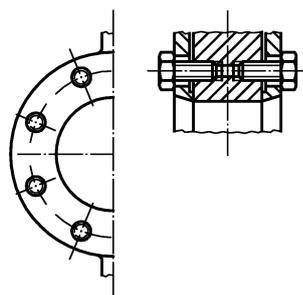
Einklemmklappe mit Flanschaugen und Gewindebohrungen
